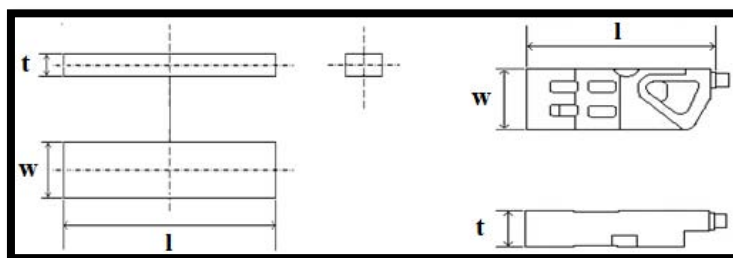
Molde utilizado para a moldação por injecção da barra, a), e cavidade moldante da barra, b).
